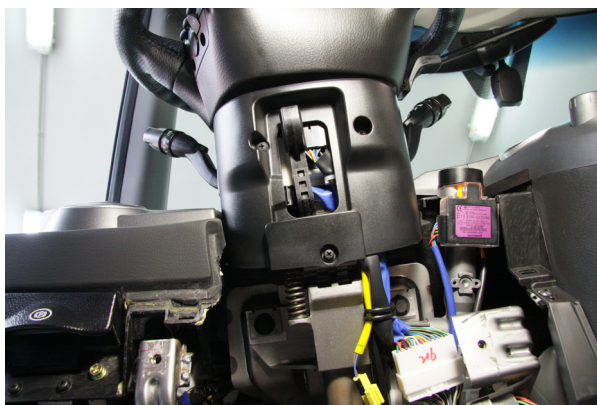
Винт и саморезы крепления рулевого кожуха
